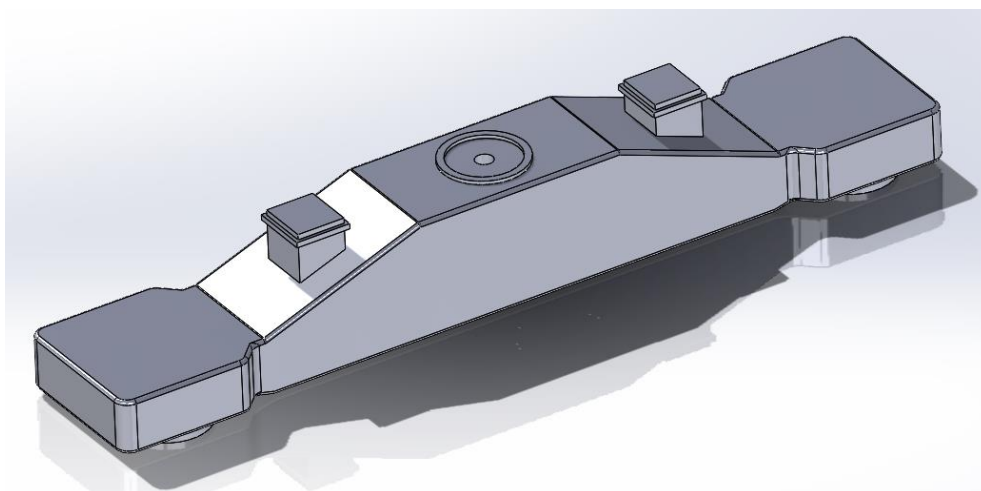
Croquis apoyo suspensión secundaria refuerzo bogie
